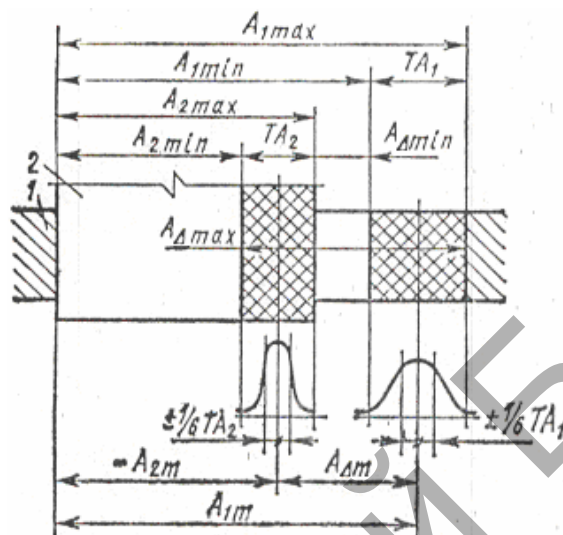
Вероятное расположение полей допусков и их величина
